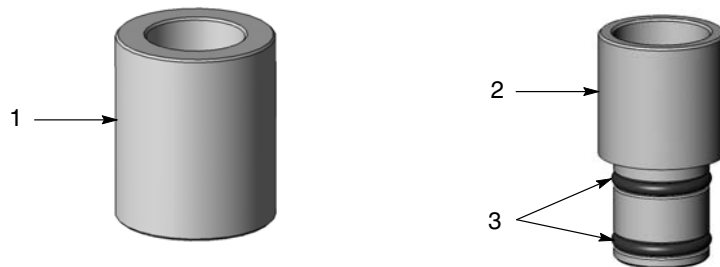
Acoplamiento y adaptador opcionales para la bomba
